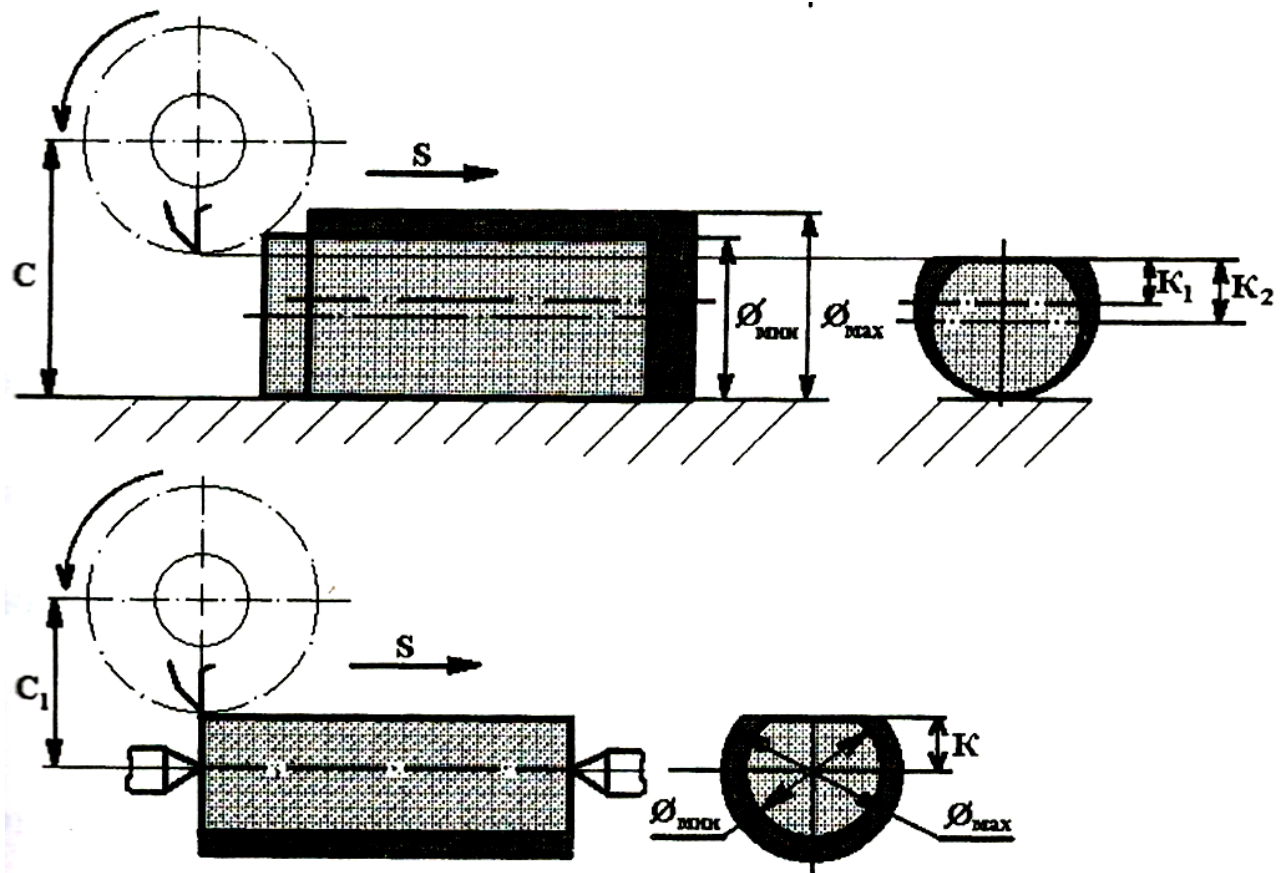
Фрезерование лыски на валу при установке вала на столе станка или в центрах
